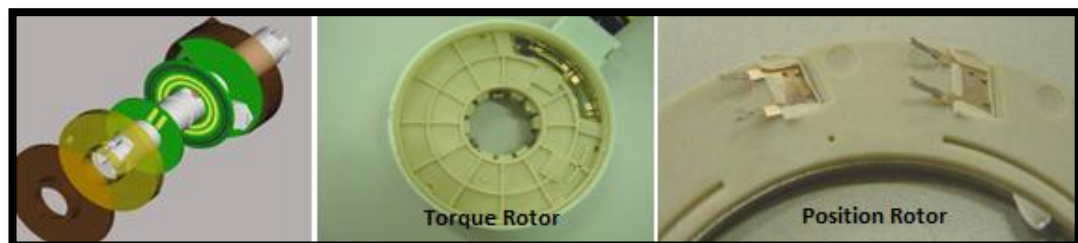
Posición de los rotores del sensor de torque Hyundai Accent MC
